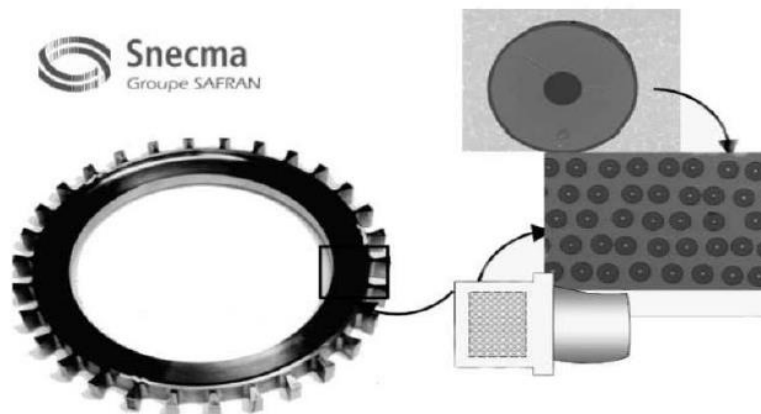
Disc de compressor de turboreactor fabricat en material compost [Ler13]
